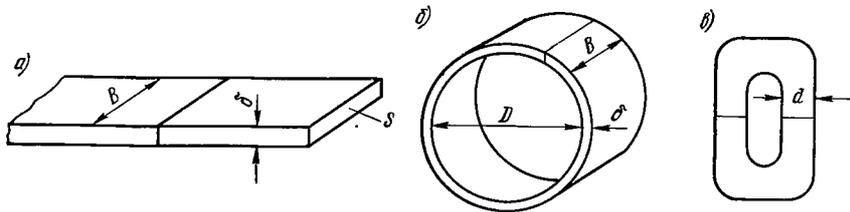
Типовые сварные стыковые соединения
